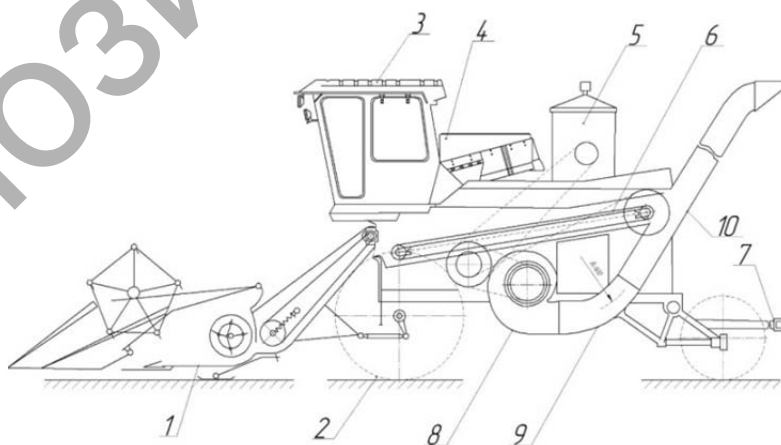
Усовершенствованная конструкция комбайна зерноуборочного самоходного КЗС-10 «ПАЛЕССЕ»: 1 — жатка; 2 — ходовая часть; 3 — кабина; 4 — верхний кожух; 5 — приёмная камера; 6 — цепочно-планчатый транспортёр; 7 — прицепное устройство; 8 — вентилятор Ц14-46; 9 — пневмопровод; 10 — выгрузной пневмопровод хлебной массы
